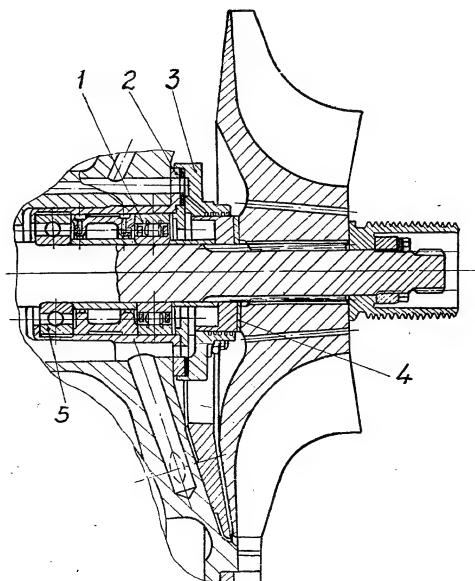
Ротор газотурбинного двигателя (разрез).
